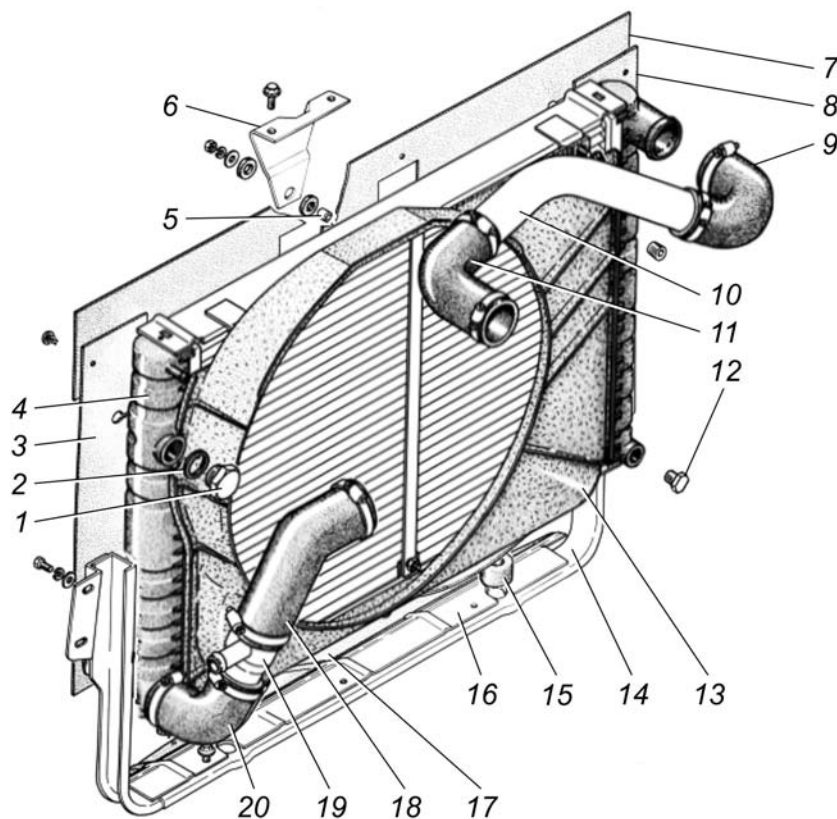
Радиатор: 1 - пробка; 2 - прокладка; 3 - уплотнитель левый; 4 - радиатор; 5 - втулка; 6 - кронштейн; 7 - уплотнитель верхний; 8 - уплотнитель правый; 9 и 11 - шланг подводящий; 10 и 19 - труба; 12 - пробка сливная; 13 - кожух вентилятора; 14 - рамка радиатора; 15 - подушка; 16 - угольник; 17 - уплотнитель нижний; 18 и 20 - шланг отводящий
